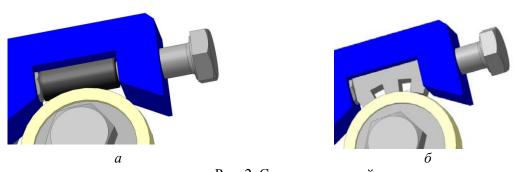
Схемы испытаний: a — схема «ролик – роликоподшипник»; δ — схема «колодка – ролик»
